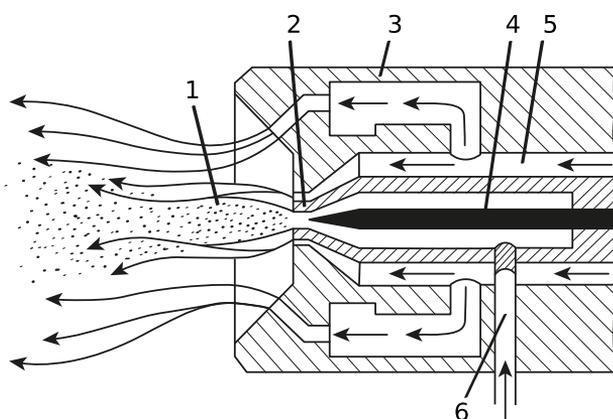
Схема форсунки для нанесения фоторезиста
